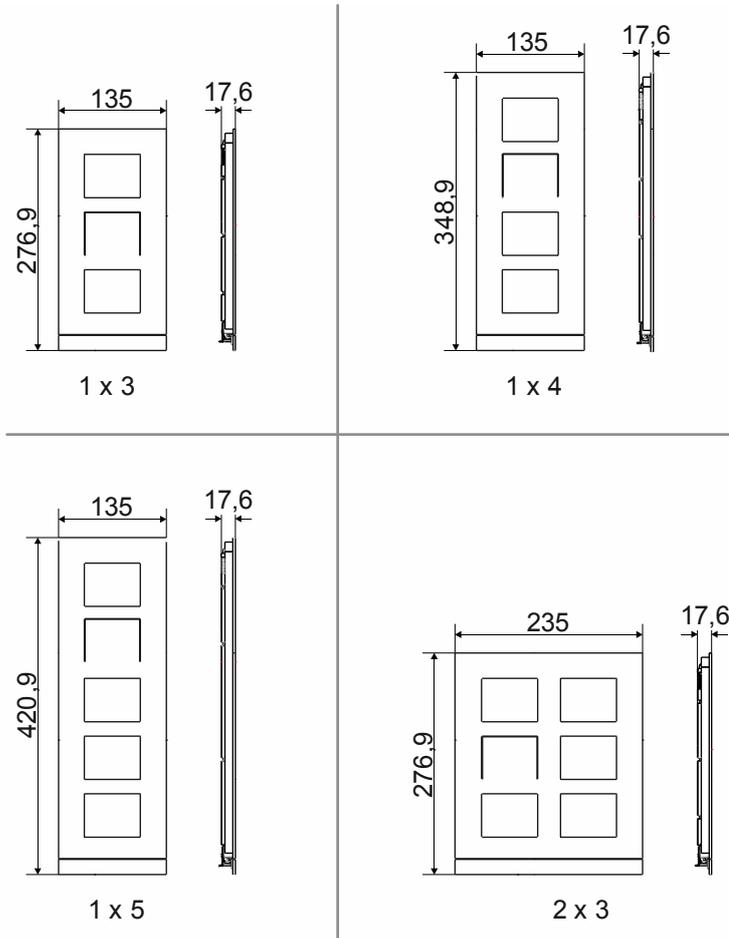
Außenmaße Außenstationen (Maße in mm)
